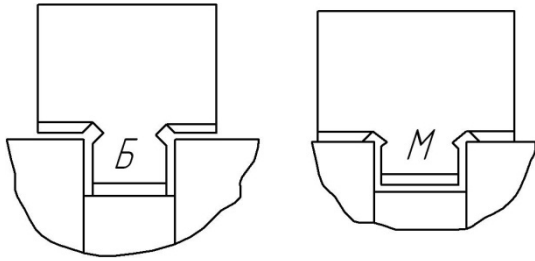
Схема измерения глубины канавки на наружной (или торцевой) поверхности шаблоном
